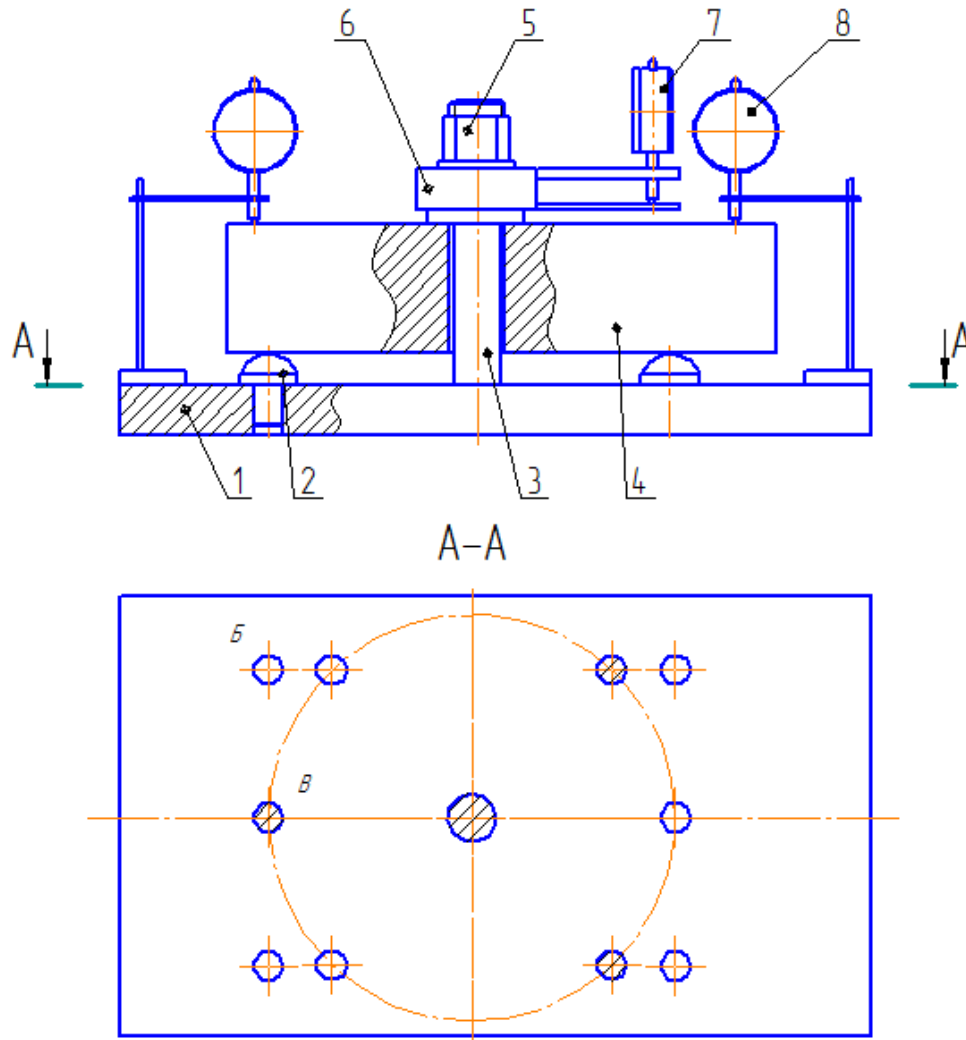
Конструктивная схема установки для определения смещений заготовки под действием сил закрепления при базировании по плоскости
